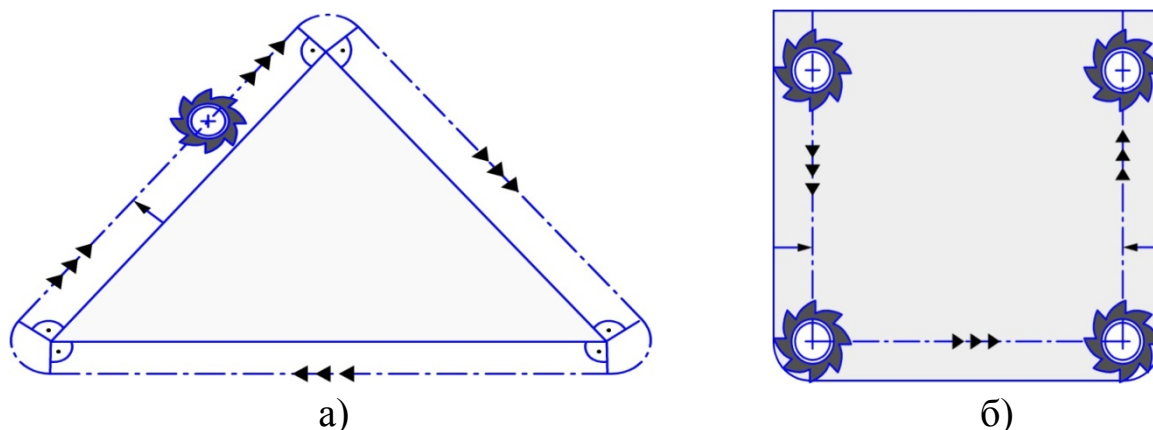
Обработка контура с наружными (а) и внутренними (б) углами
